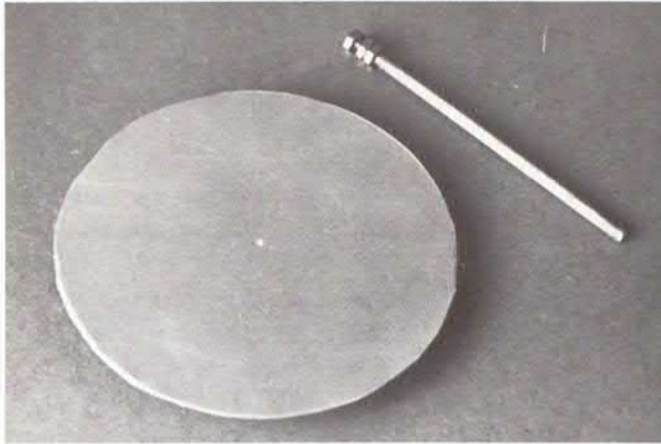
Zusatzmaterial: Aluminiumblech und Welle mit Gewinde
